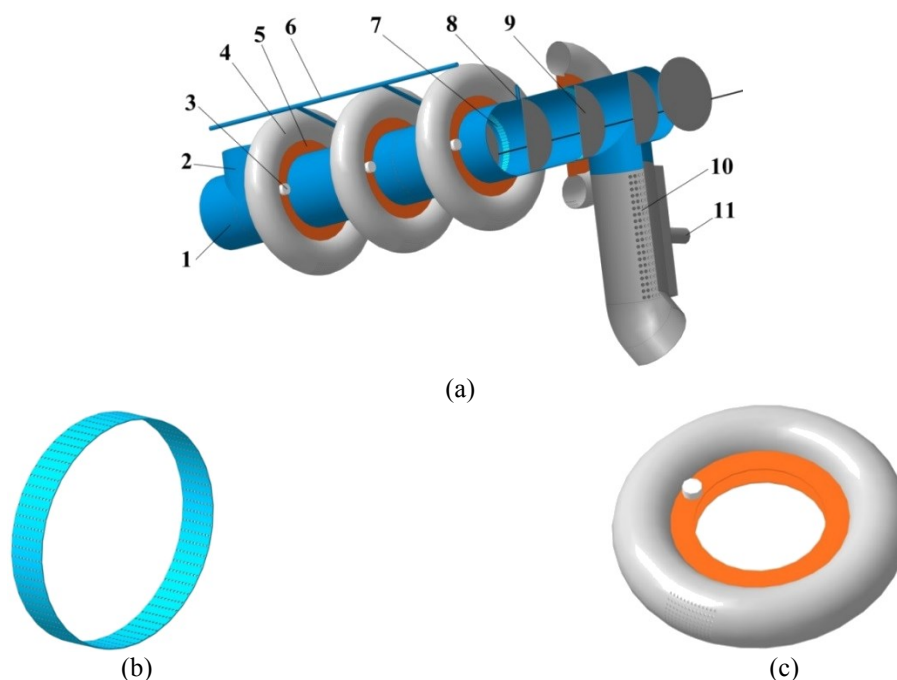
СВЧ установка с тороидальными резонаторами для отделения волосяного покрова от кожи шкур кроликов в процессе распыления рассола: (а) общий вид в разрезе; (б) диэлектрическая перфорированная муфта; (с) тороидальный резонатор; 1 – направляющая труба тросо-шайбового транспортера; 2 – загрузочный патрубок; 3 – магнетрон; 4 – тороидальные резонаторы; 5 – центральная часть тороидального резонатора; 6 – трубопровод для подачи рассола; 7 – муфты перфорированные, диэлектрические; 8 – распылители рассола; 9 – тросо-шайбовый транспортер, диэлектрический; 10 – выгрузной патрубок перфорированный; 11 – пневмопровод
